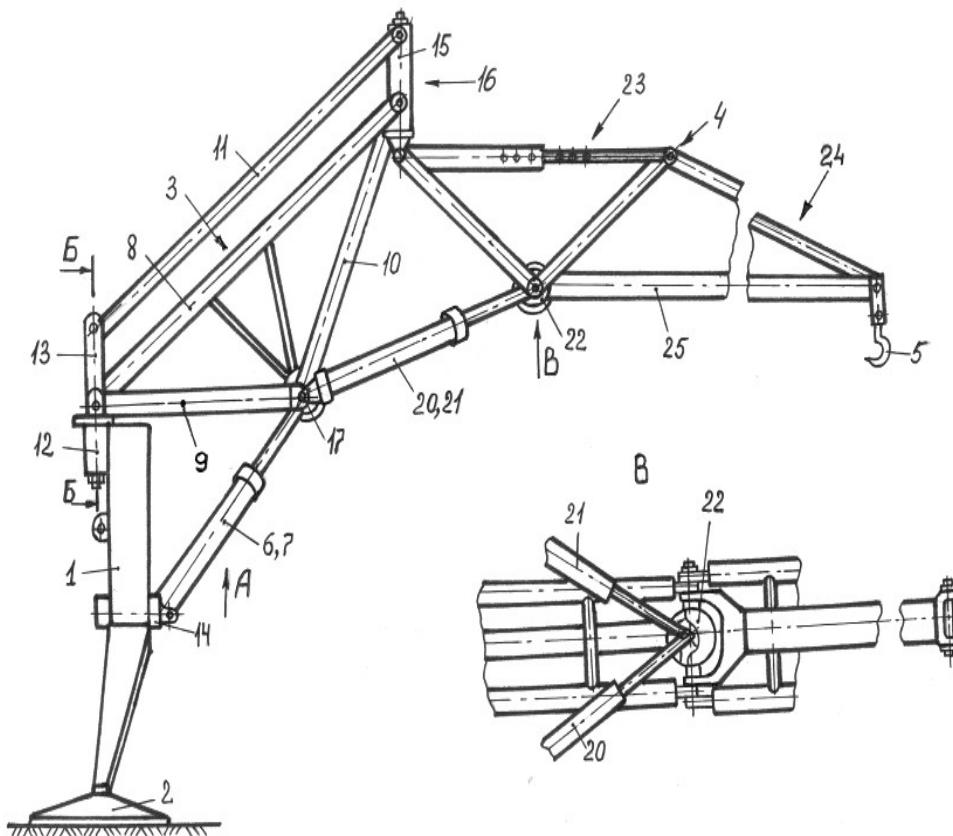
Шарнирно-стержневой гидроманипулятор с двумя пространственными приводными механизмами
